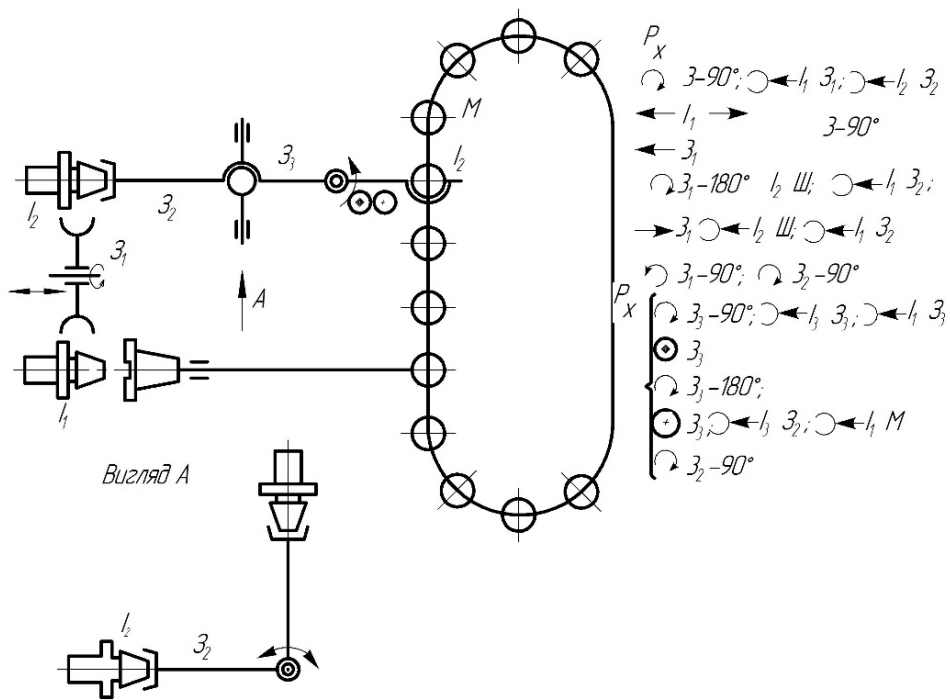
Механізми з захватними пристроями біля шпинделя
